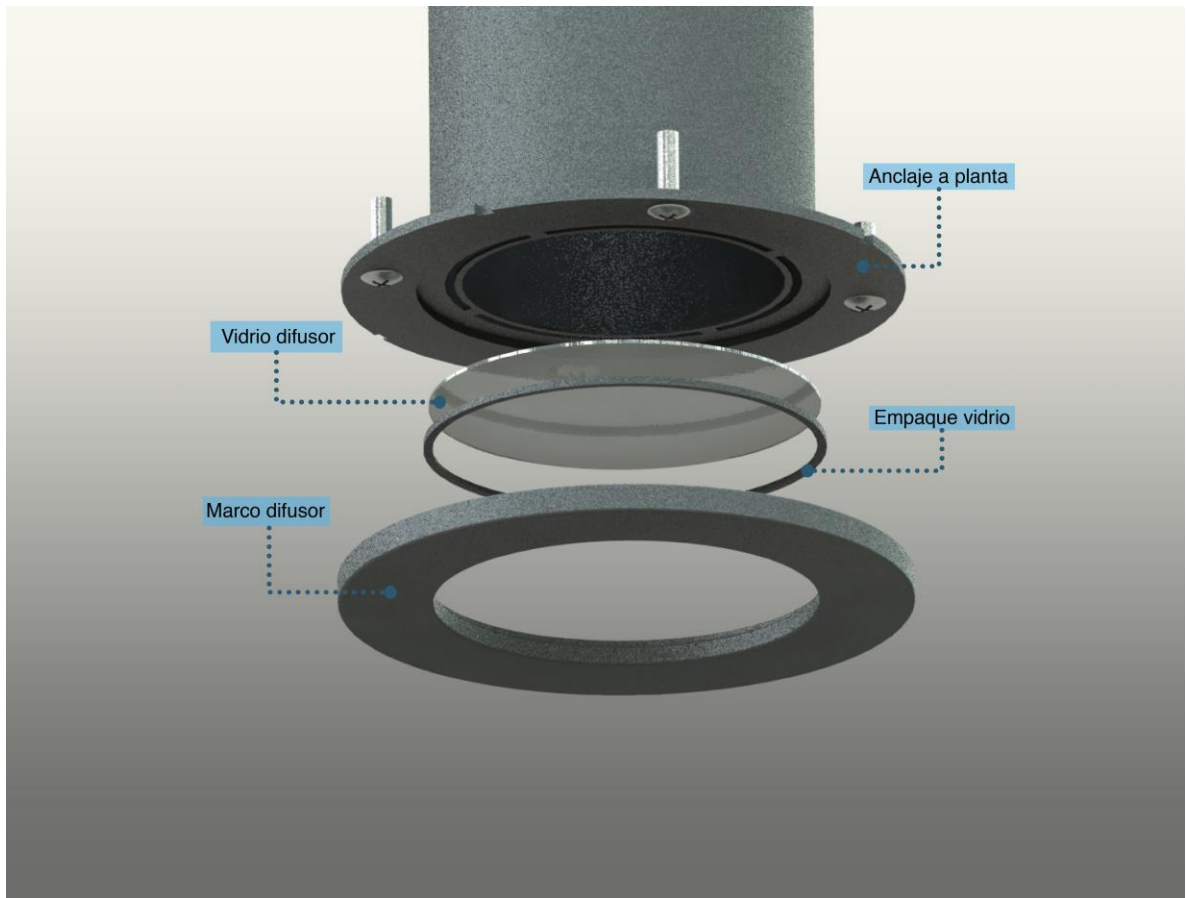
Vista explosionada difusor. Fuente: Autora.
